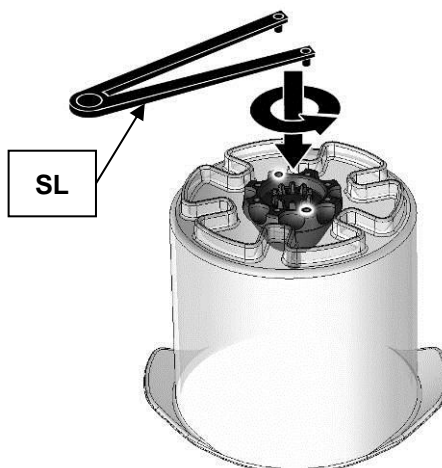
Удаление колпачка ножа с помощью торцевого штифтового гаечного ключа
